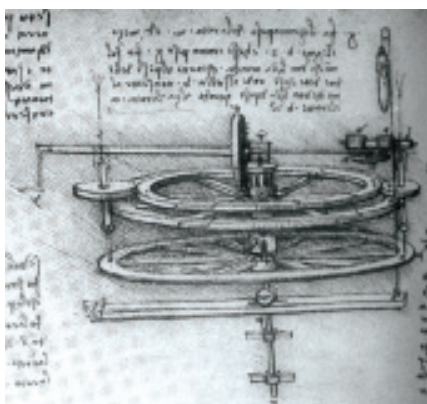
Leonardo. Macchina tessile per la bobbinatura.
